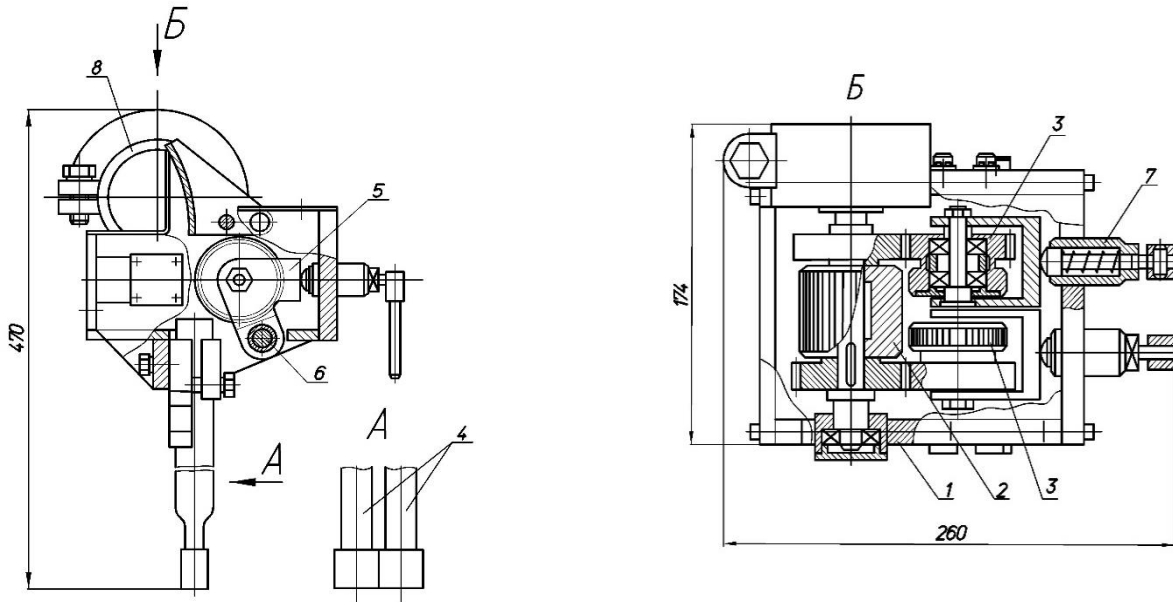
Пристрій для наплавлення двома стрічковими електродами
